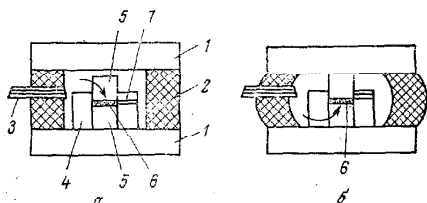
Схема конструкции вакуумной пресс-формы [242]:
